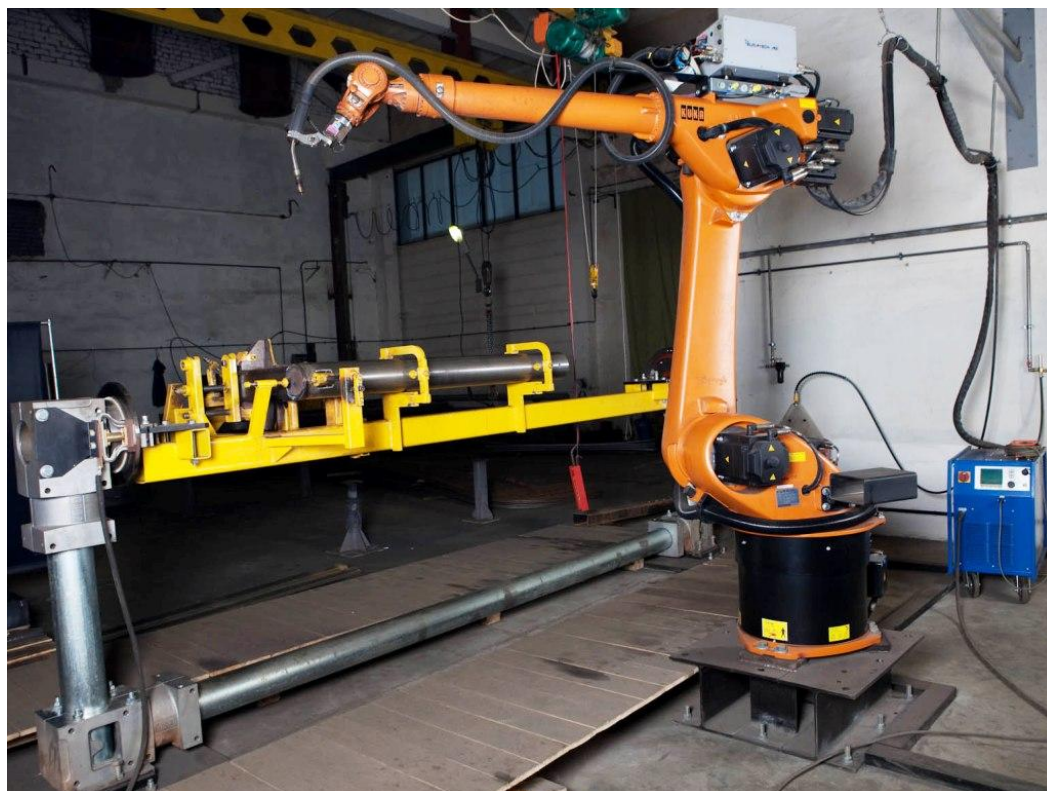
Сварочный робот фирмы Кука с двигателями кисти на дальнем конце локтевого звена манипулятора [64]
